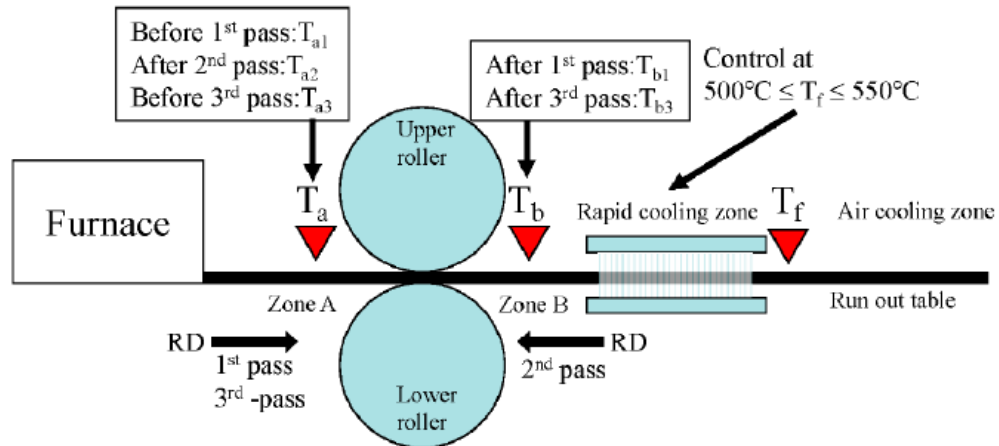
Схема горячей листовой прокатки за 3 прохода [134]
